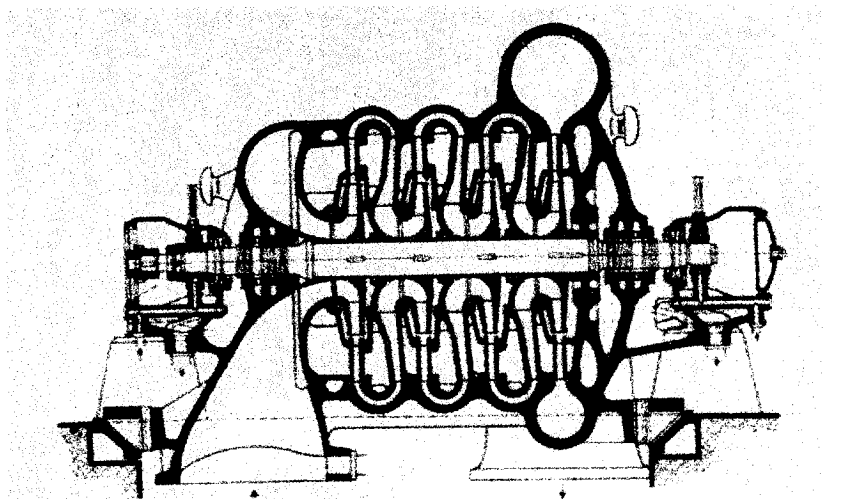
Проточна частина відцентрового компресора фірми Зульцер
